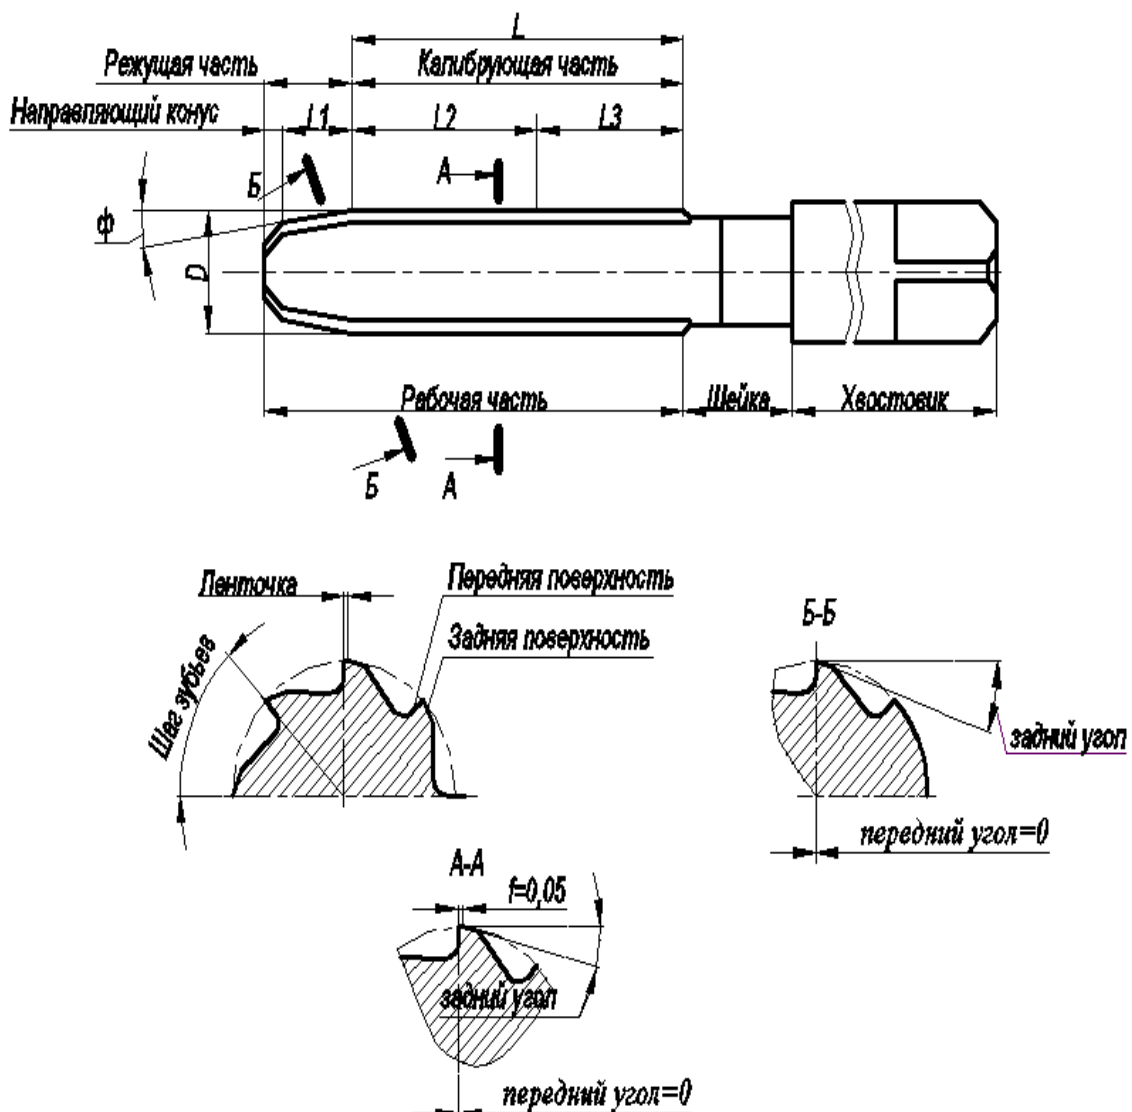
Конструкция ручной цилиндрической развёртки
